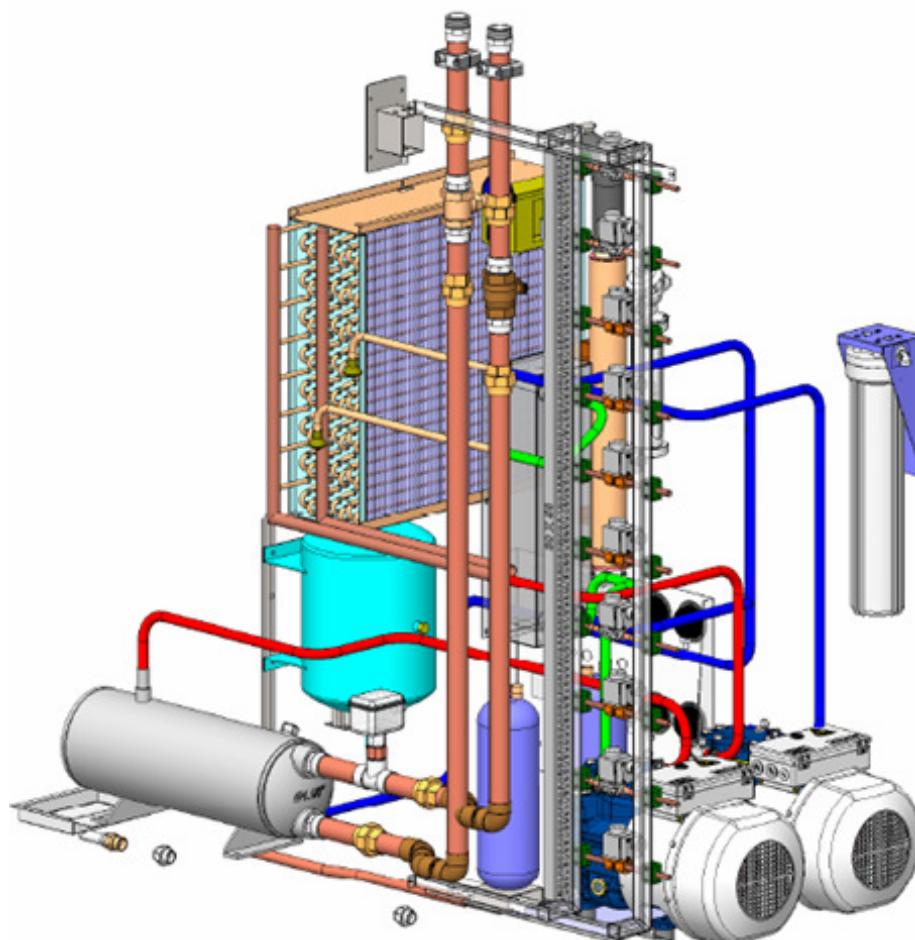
Exemplo de Desenho de Fabricação Mecânica
